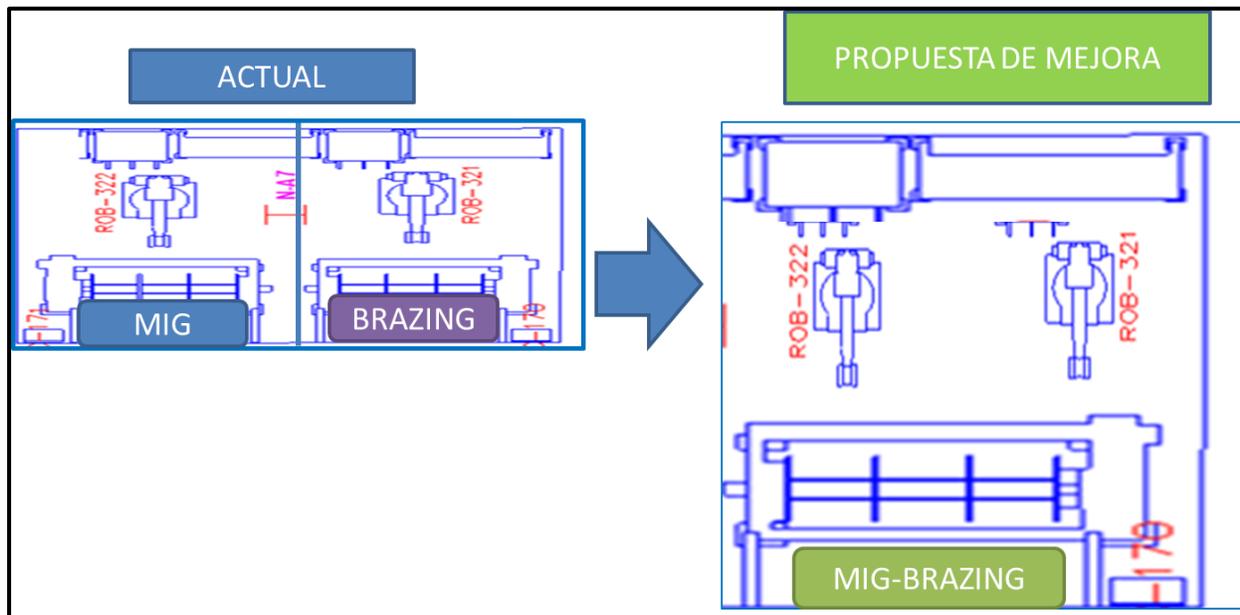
Propuesta de unificación de celdas de procesos de soldadura MIG y BRAZING. Fuente: propia.
